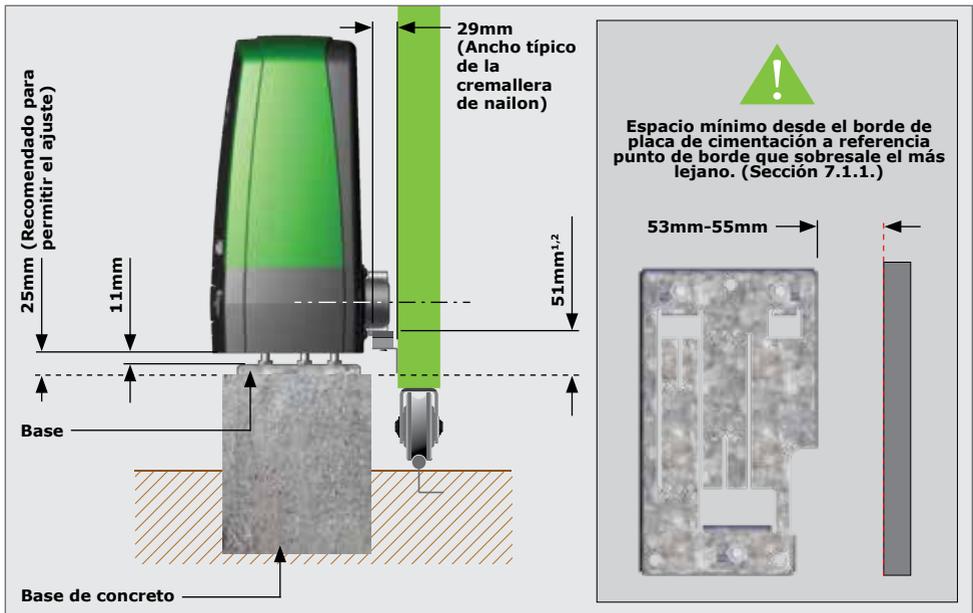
CREMALLERA DE NAILON SOBRE EL PIÑÓN
